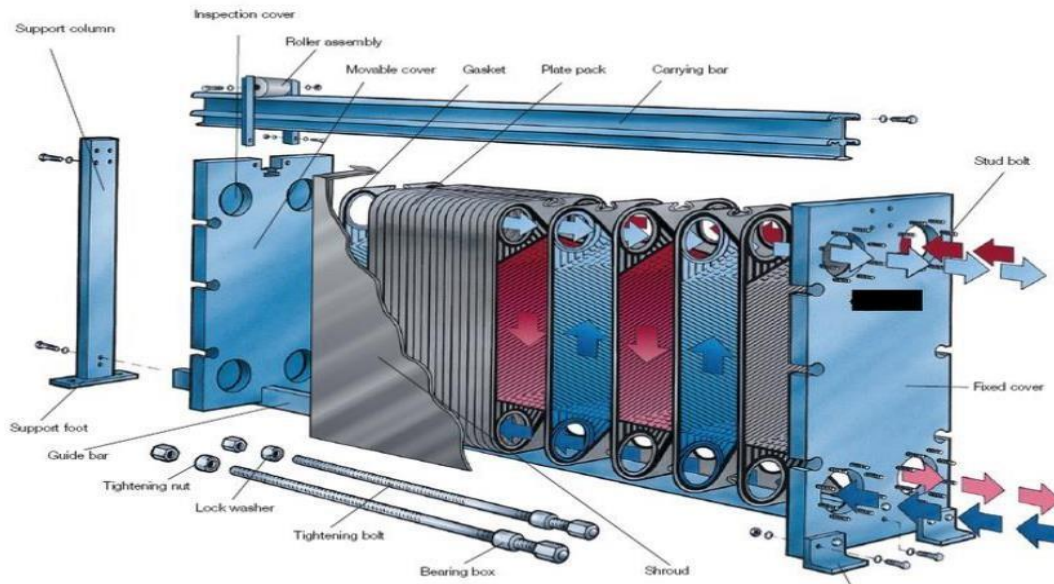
Plan éclaté d'un échangeur plaque et joints.
